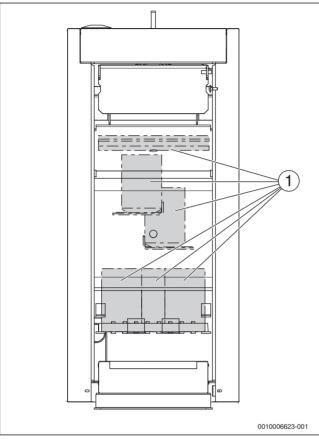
Lage der Feuerraumsteine im Feuerraum (Frontansicht)
